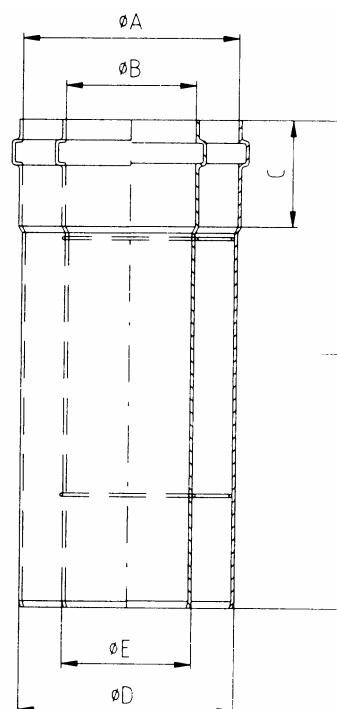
Průchod rovnou střechou pro soustředný komín Ø 125/80 mm
